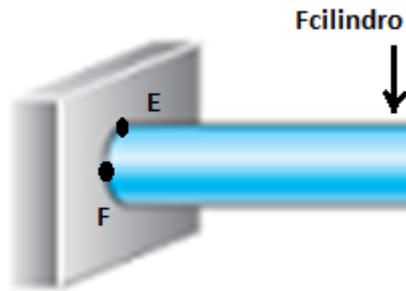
Puntos críticos de la soldadura en el empotramiento.
